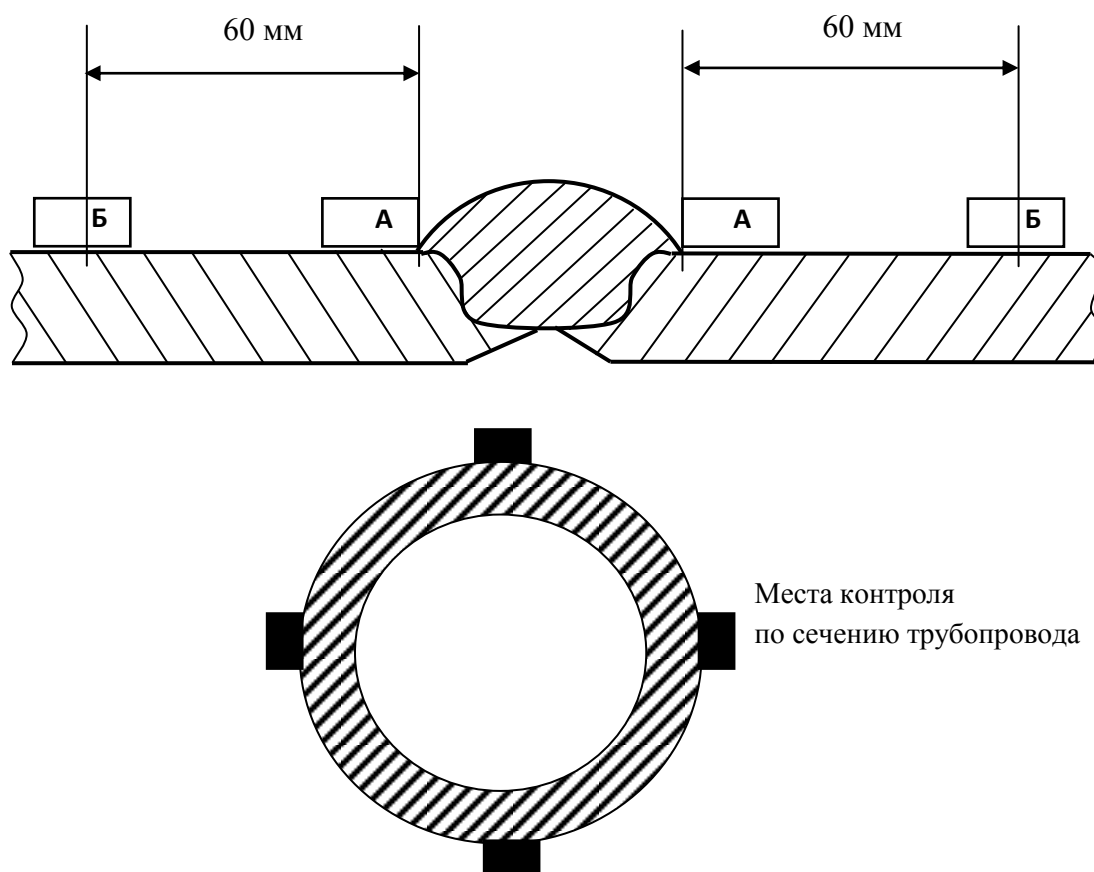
Расположение точек измерения относительно валика усиления сварного шва:
